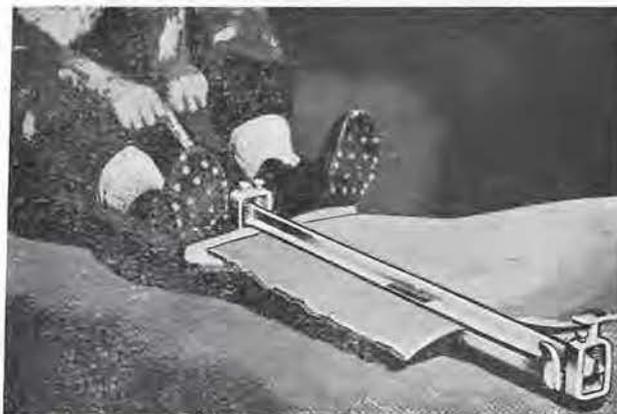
Machine «Comet» fixée sur la bande. L'ouvrier tire la poignée et réalise la coupe.
